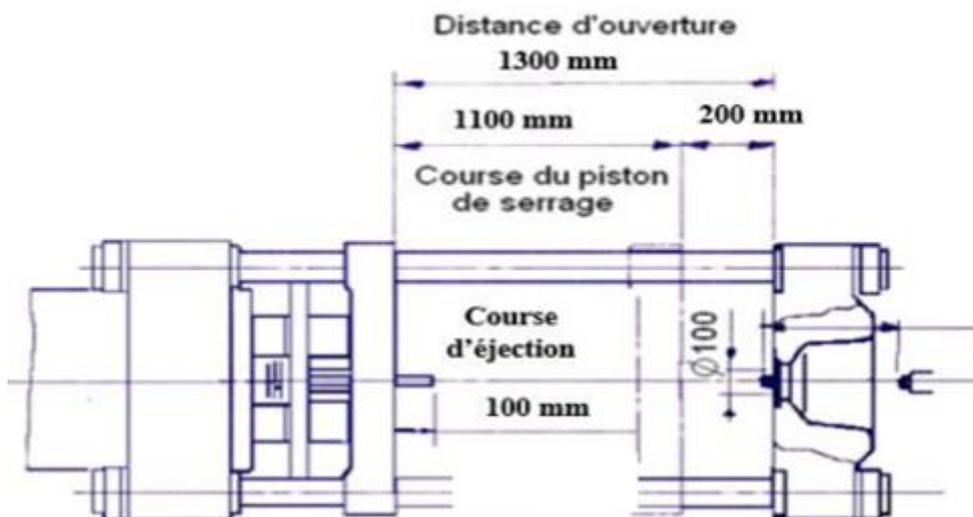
Caractéristiques dimensionnelle de la presse 225 T [11].
